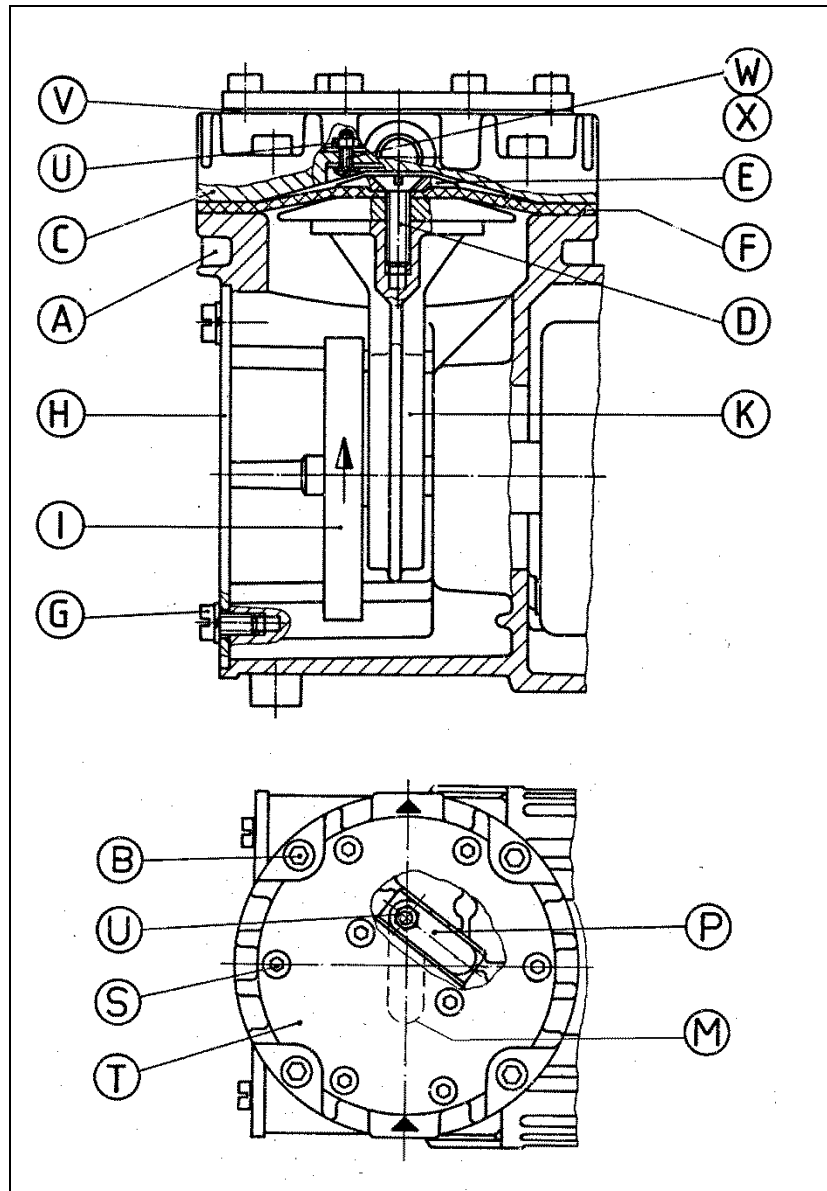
Pumpenteile für Ausführungen mit Aluminiumkopf
